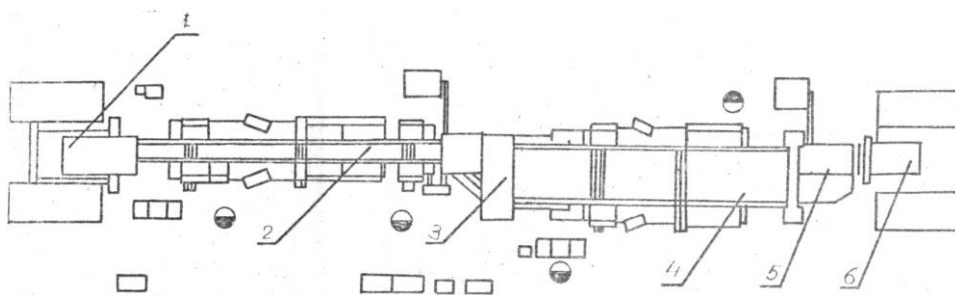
Схема лінії для форматної обробки й облицювання крайок щитів: 1 - вакуумний накопичувач; 2 - верстат комбінований для форматного обрізання й облицювання поздовжніх крайок; 3, 5 - поворотний пристрій; 4 - верстат комбінований для форматного обрізання й облицювання поперечних крайок; 6 - укладальник вакуумний
